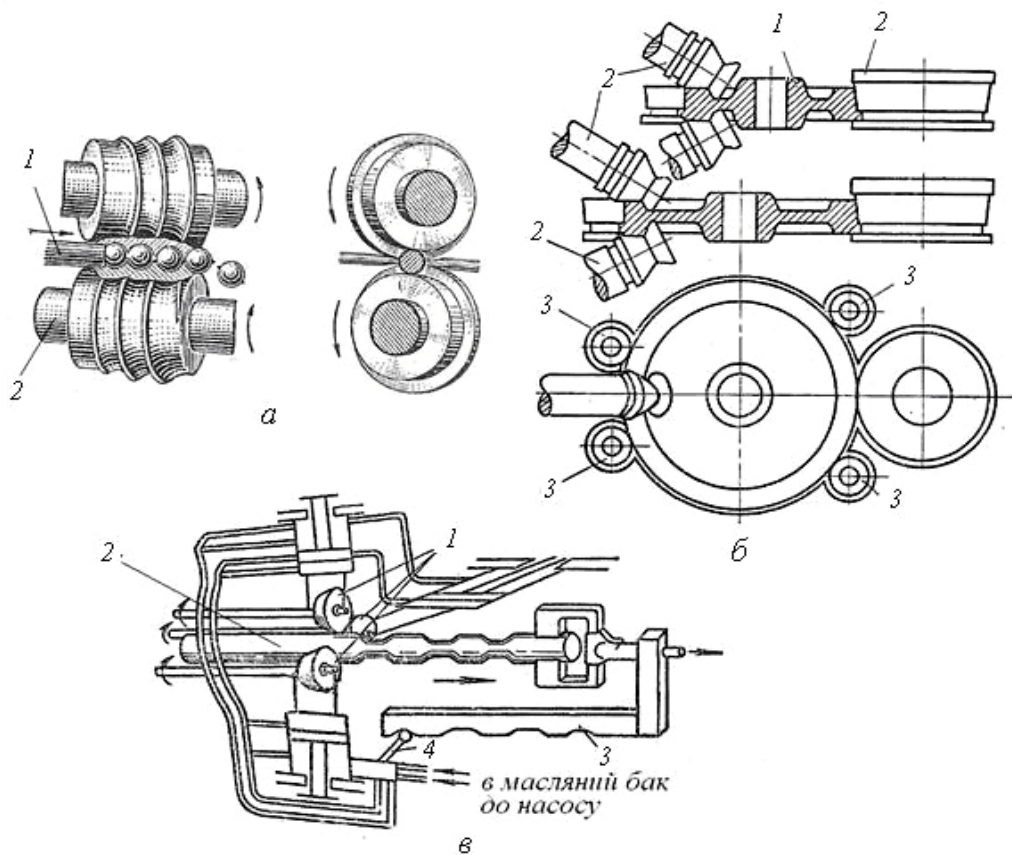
Схема прокатування на поперечно-гвинтових станах: а-прокатування куль (1 – заготовка, 2 валки); б-прокатування бандажів і коліс (1 – заготовка, 2 – конусні робочі валки, 3 – опорні валки); в-прокатування періодичного профілю (1 – робочі валки, 2 – заготовка, 3 – копіювальна лінійка, 4 – щуп)
